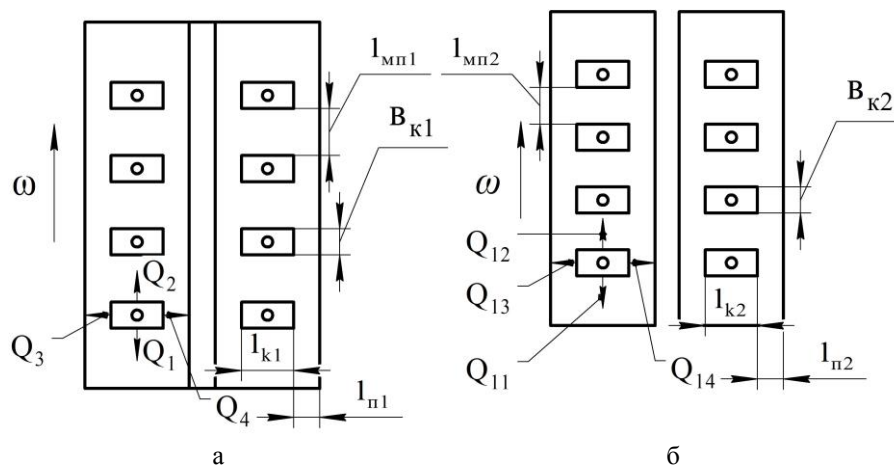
Развертки наружной (а) и внутренней (б) рабочих поверхностей подшипника
